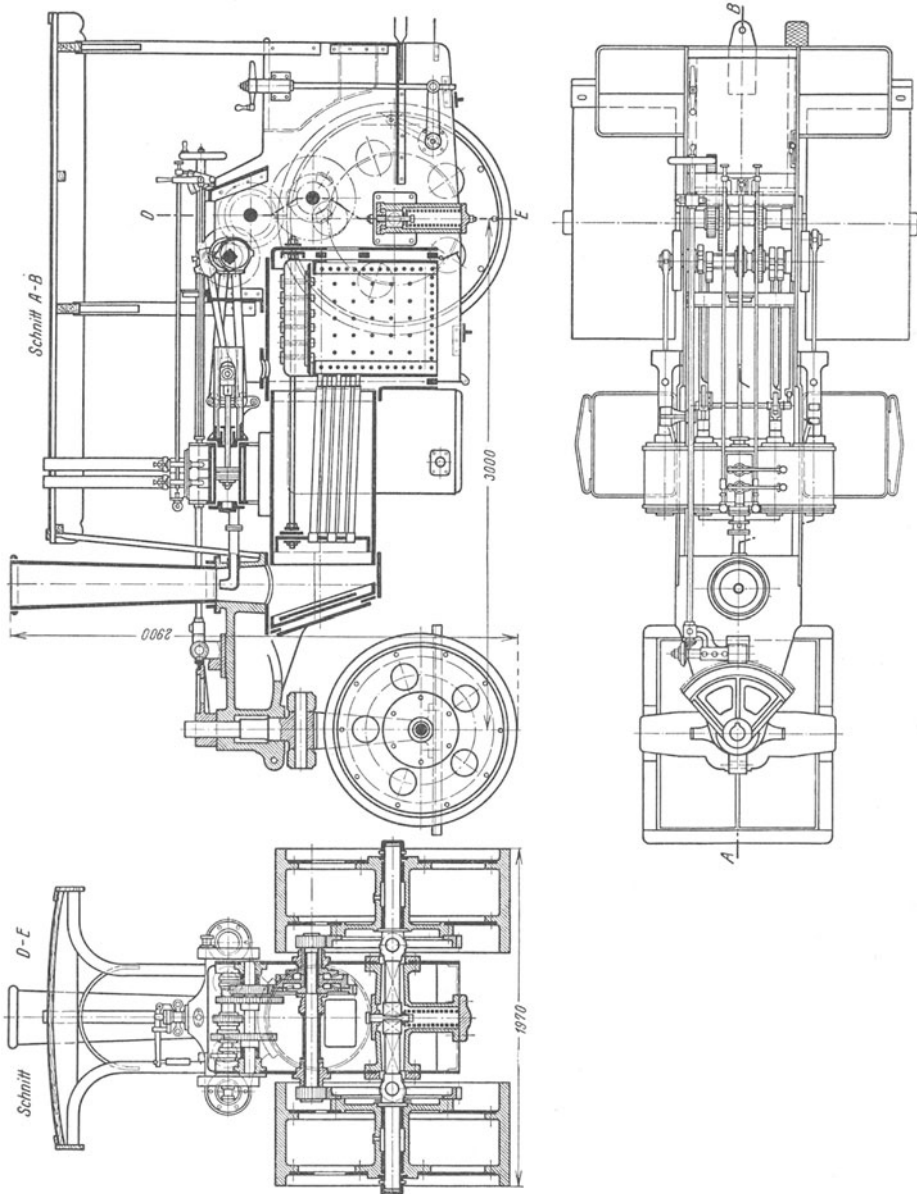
Dampfstraßenwalze der Maschinenfabrik Ruthemeyer Soest.
